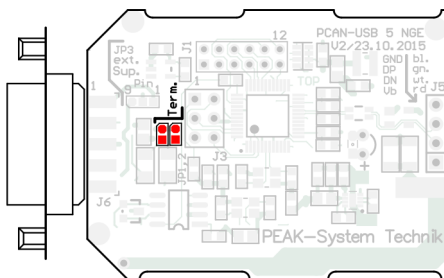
Platine PCAN-USB (IPEH-002021) ab Ser.-Nr. 200000, Lötfelder für CAN-Bus-Terminierung
